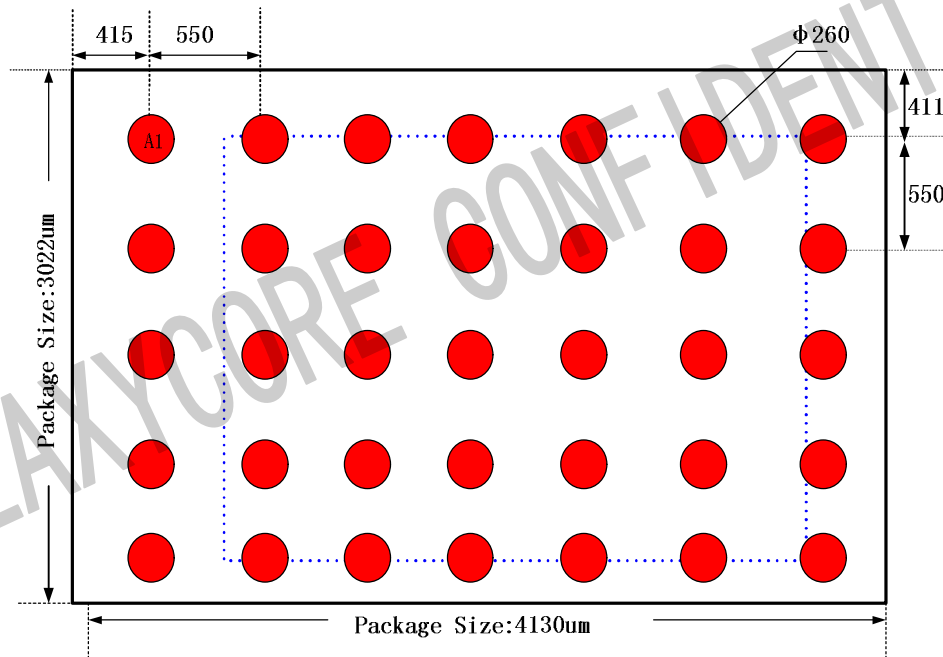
PCB 焊盘设计说明示意图(Top View)
